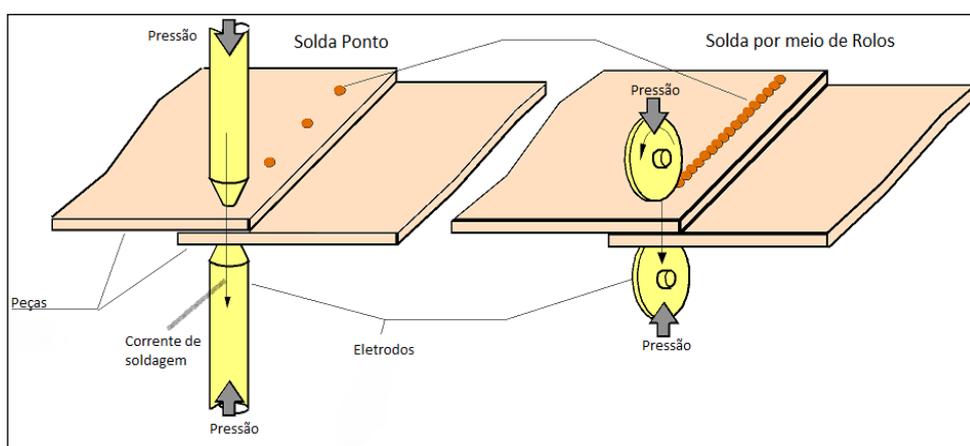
Soldagem por resistência a ponto e por meio de rolos
